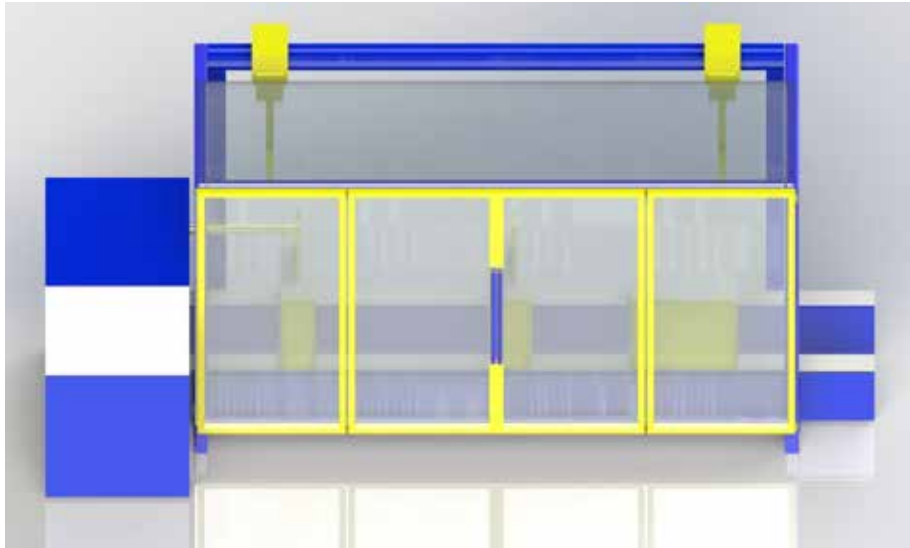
Protector para Máquina de Soldar (Vista de Frente)
